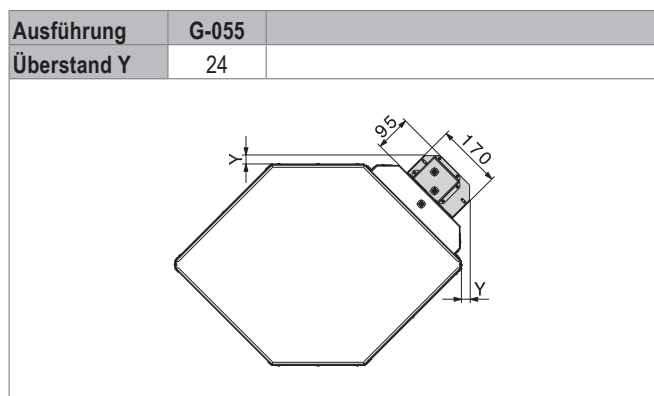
Massblatt Adapter für Gotthard G-055 (in mm)
